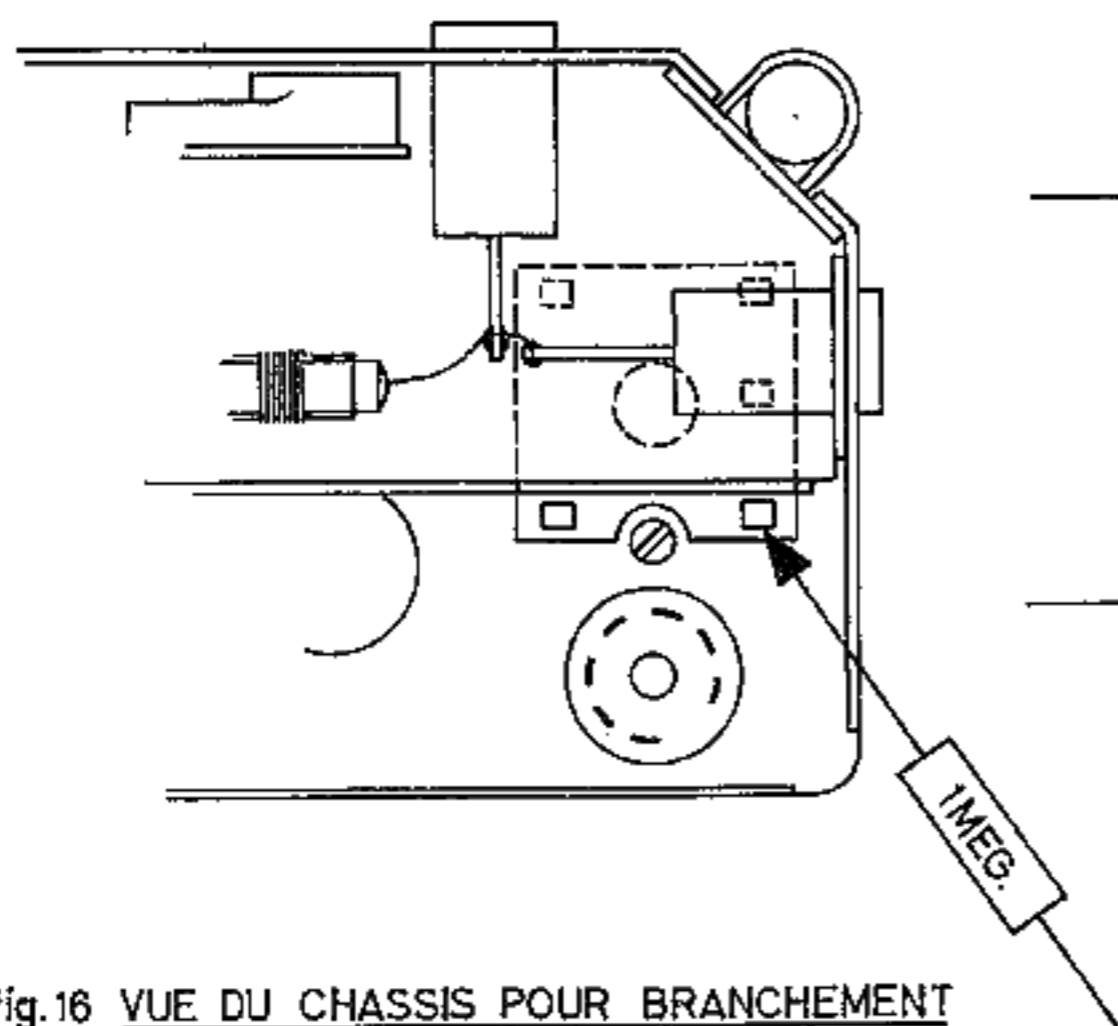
VUE DU CHASSIS POUR BRANCHEMENT DE L'OUTPUTMETRE
